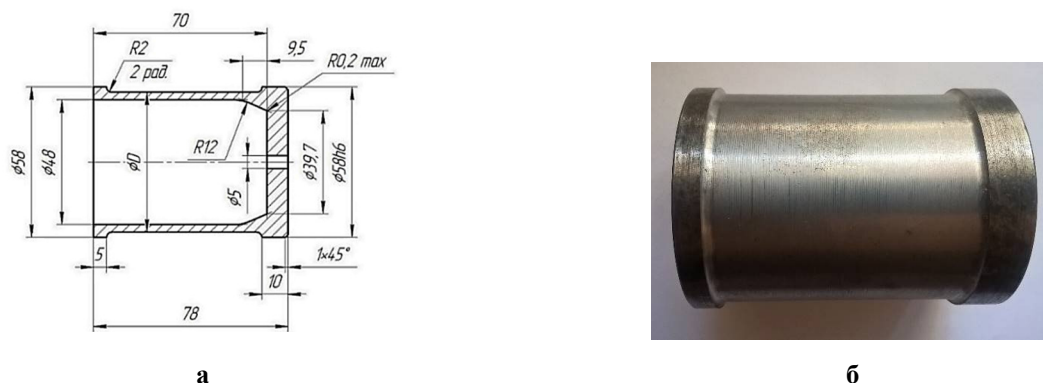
Заготовки для ротаційного видавлювання: а - ескіз заготовки, б – вихідна заготовка, яка отримана точінням з прокату
